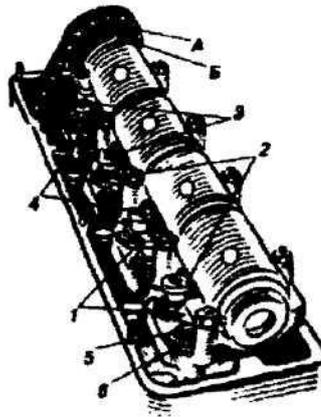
Проверка и регулировка тепловых зазоров клапанов механизма газораспределения двигателя ВАЗ-2101:
